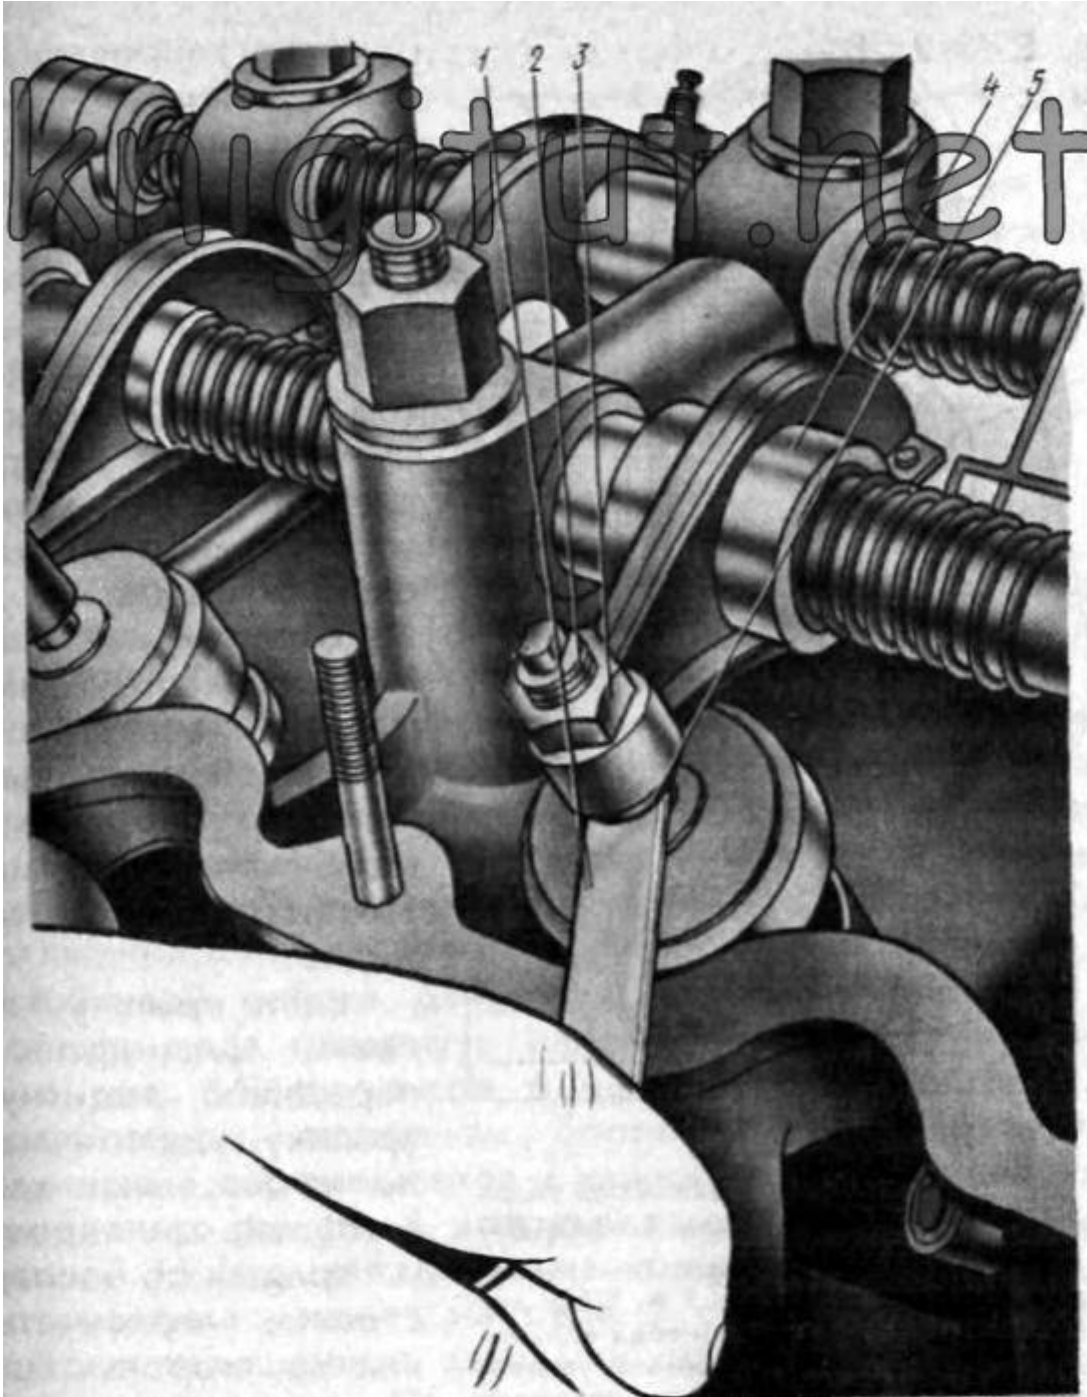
Проверка и регулировка зазоров в механизме привода клапанов двигателя «Москвич-412»: 1 - плоский щуп, 2 — регулировочный винт коромысла, 3 - контргайка, 4 — коромысло, 5 — наконечник винта
